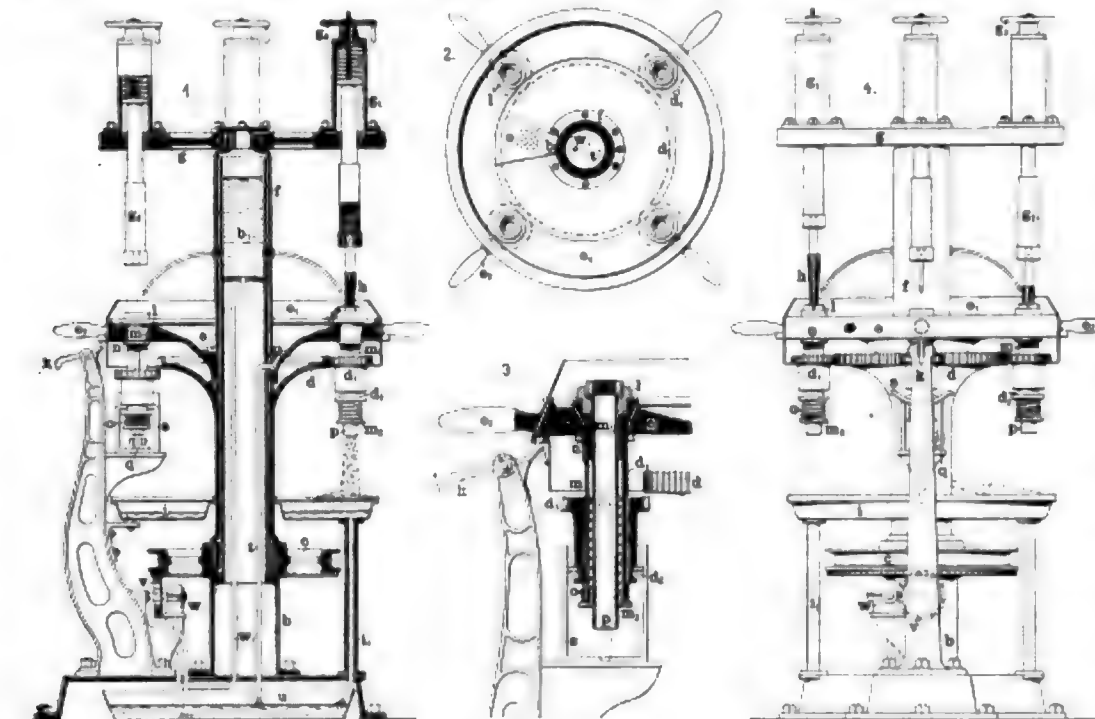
Maschine zum Schneiden von Gewinde in Schraubenmuttern.
